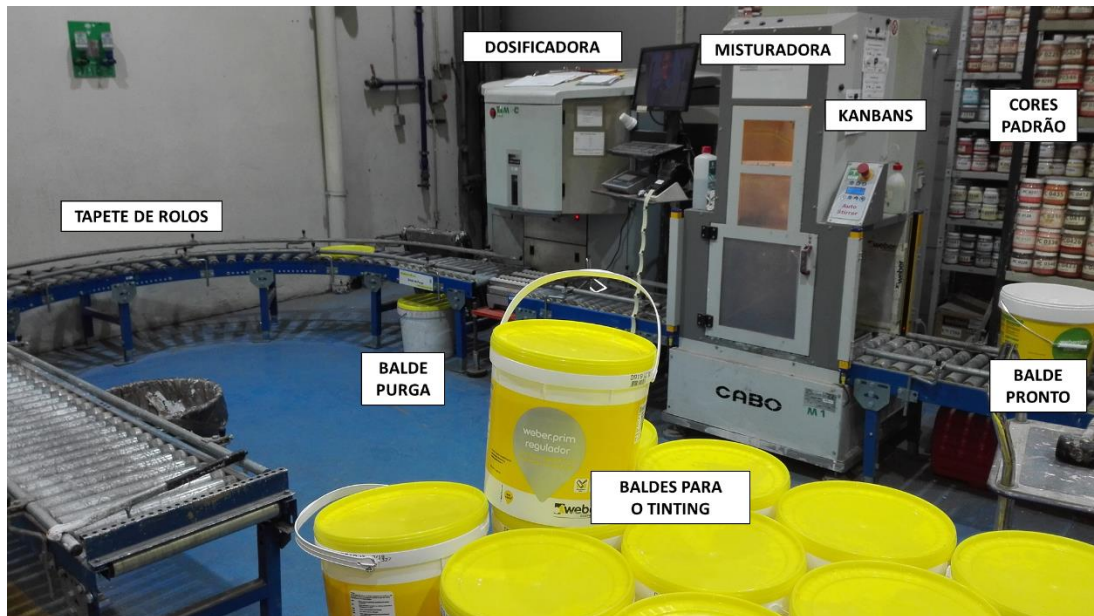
Layout geral da linha de Tinting de Aveiro.
